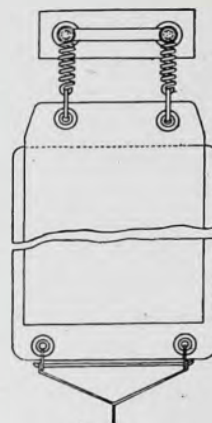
Plan de la lame adhérente du haut-parleur.
